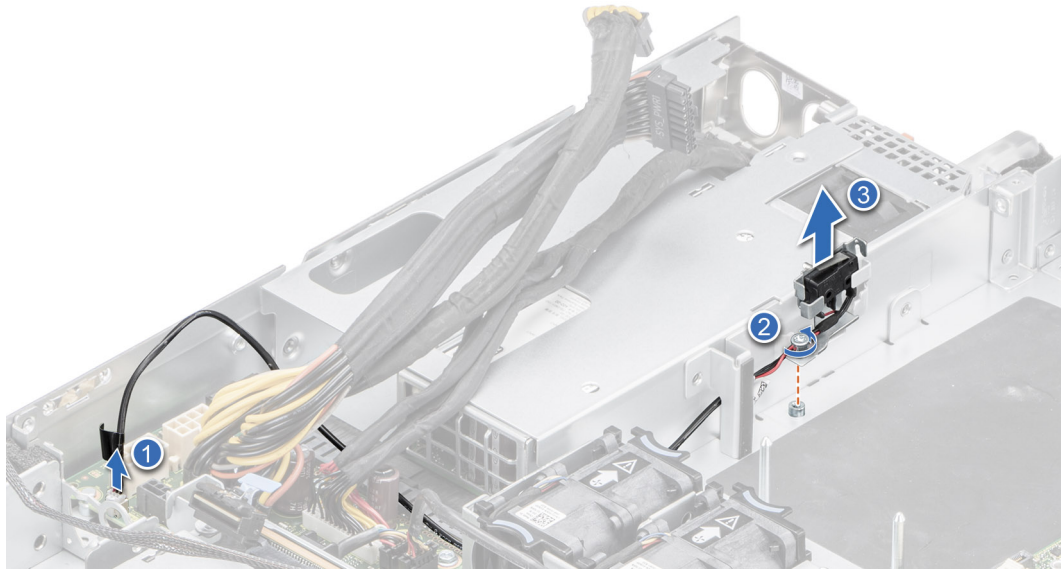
Entfernen des Eingriffsschaltermoduls
